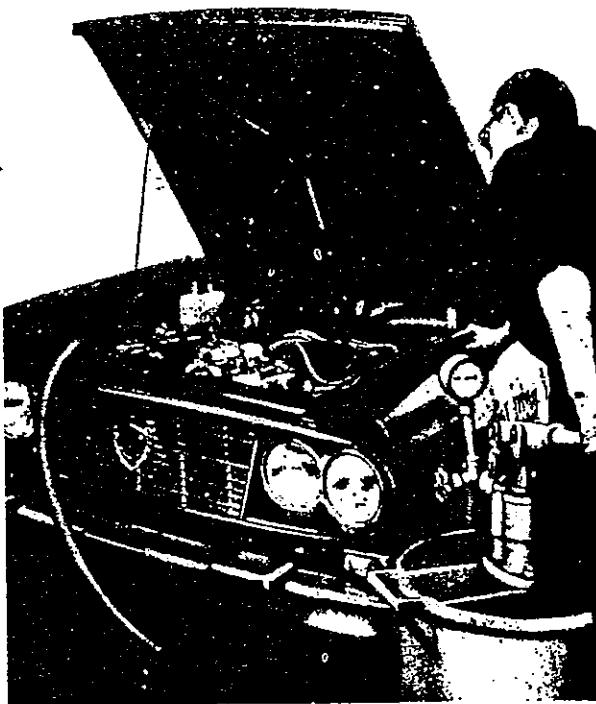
/19 - Essai sous pression de l'étanchéité hydraulique de la culasse et du bloc-cylindres.
